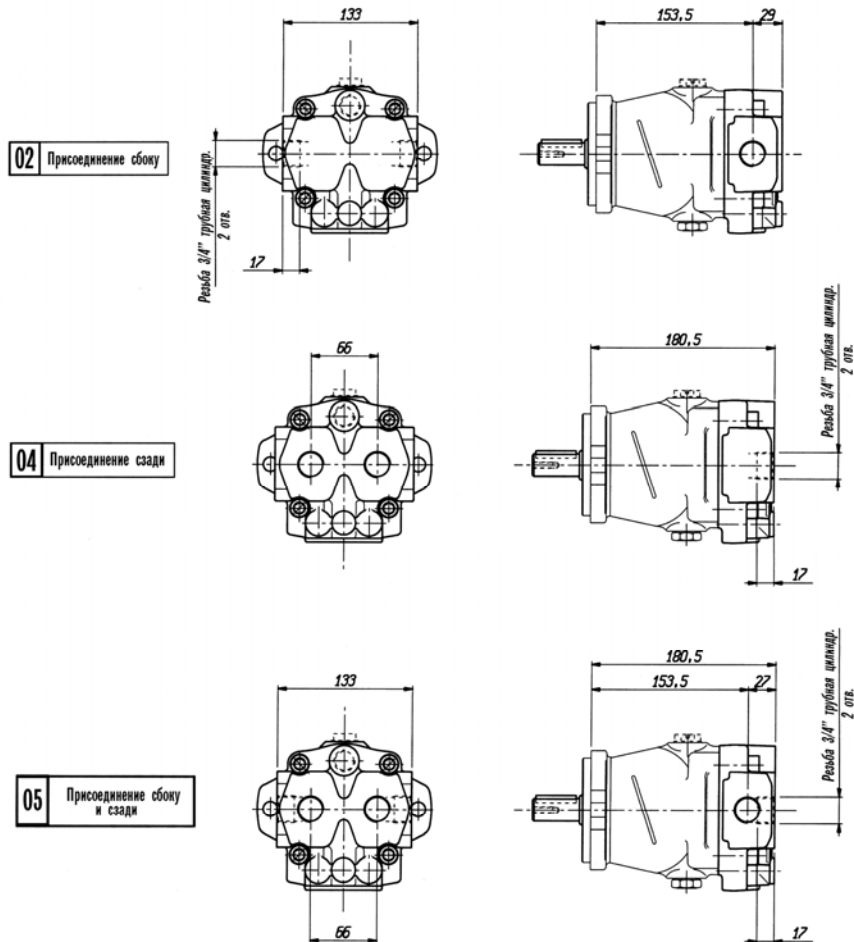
Присоединения трубопроводов к гидромотору типа M2
